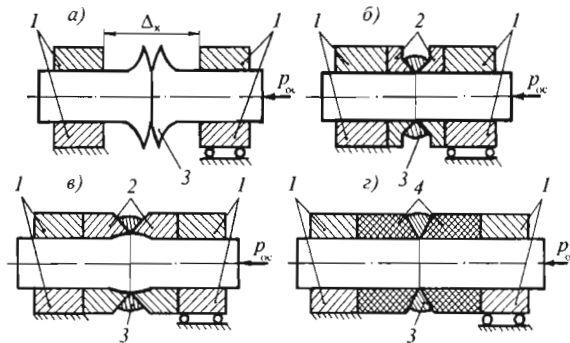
Схемы осадки при стыковой сварке:
